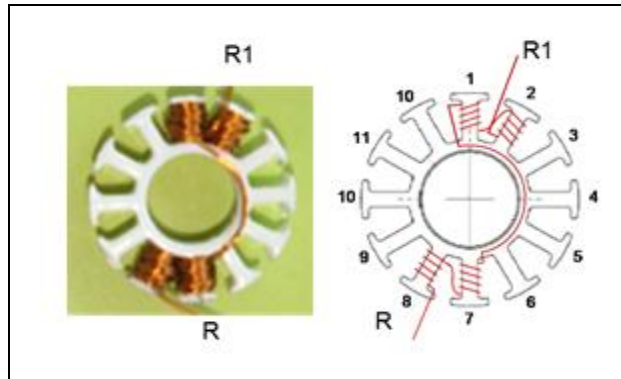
Bobinagem da fase R-R1, do estator sinterizado em bloco único de Fe1%P do mini-motor.
